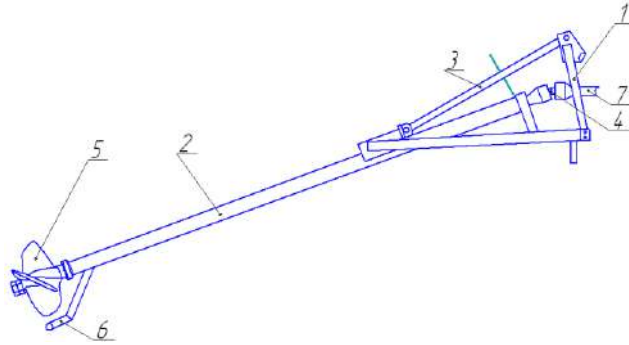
Общий вид гомогенизатора навесного: 1-навеска; 2-рама; 3-талреп; 4-вал; 5-винт; 6-упор; 7-карданный вал
